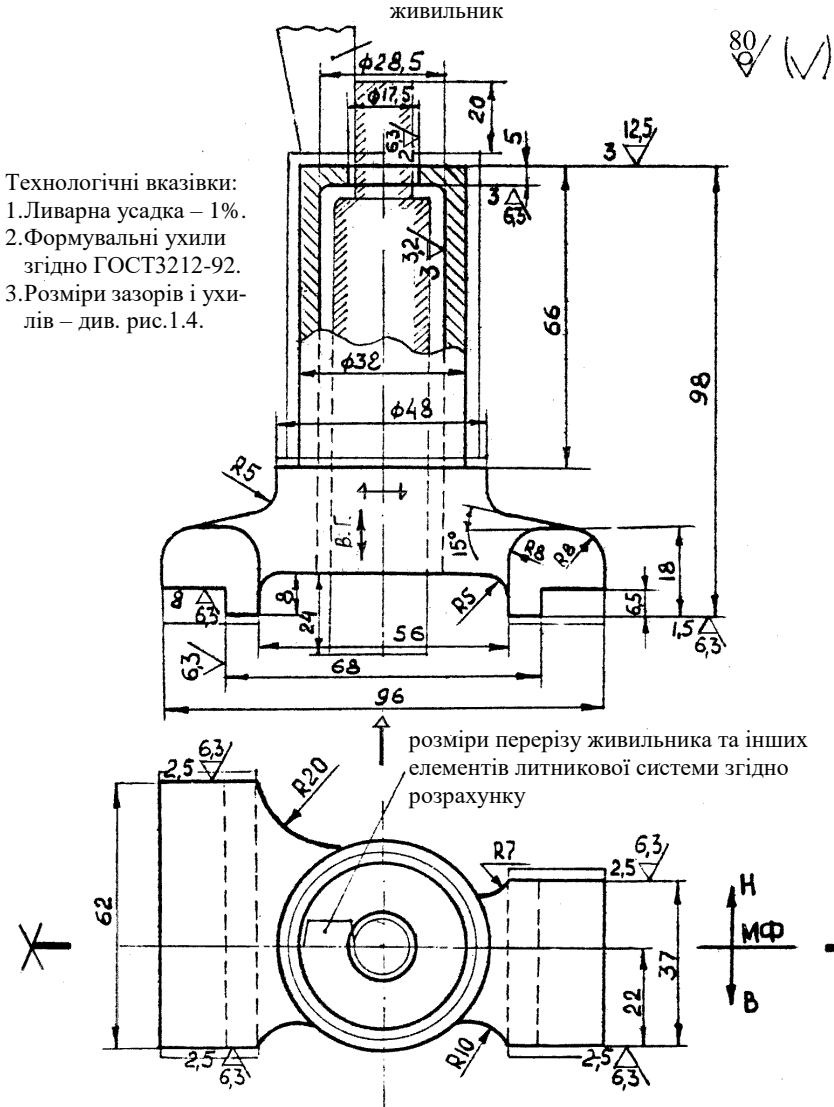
Елементи ливарної форми (для виливка “Супорт”)
